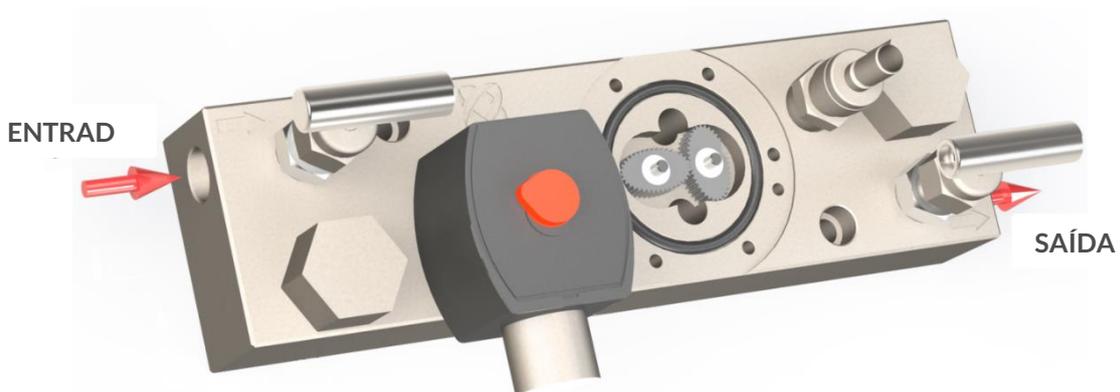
Vista perpendicular da instalação incorreta do MetroBlock com grau de inclinação.
